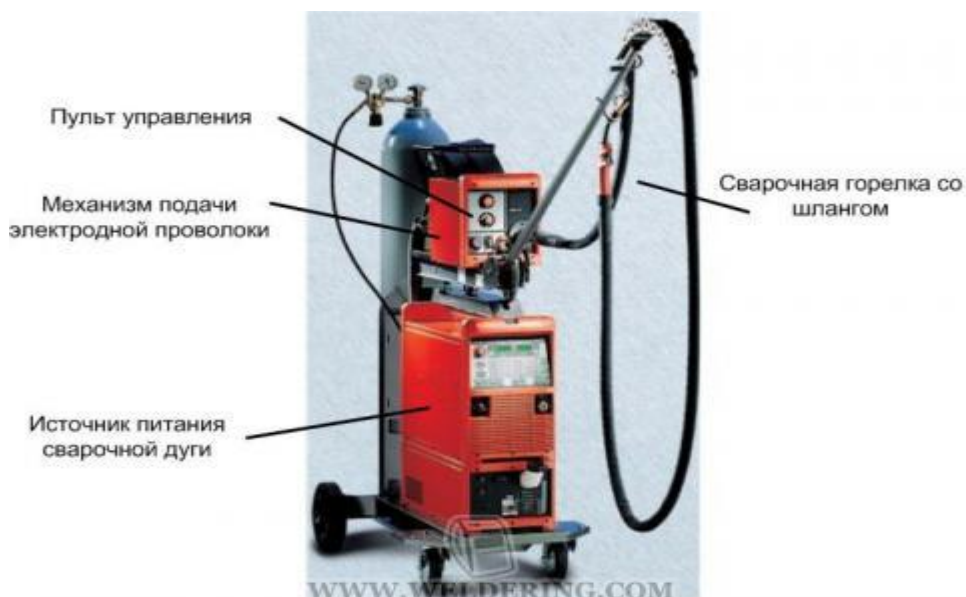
Типичный внешний вид сварочного механизированного аппарата для сварки МИГ/МАГ
